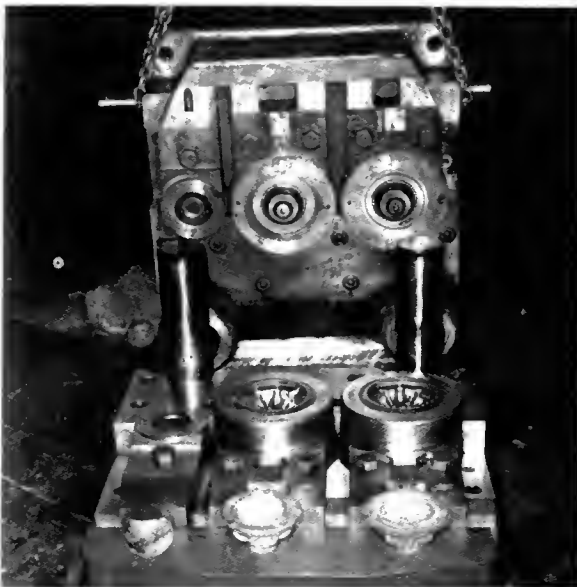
Porte-outils et outillage de presse verticale
